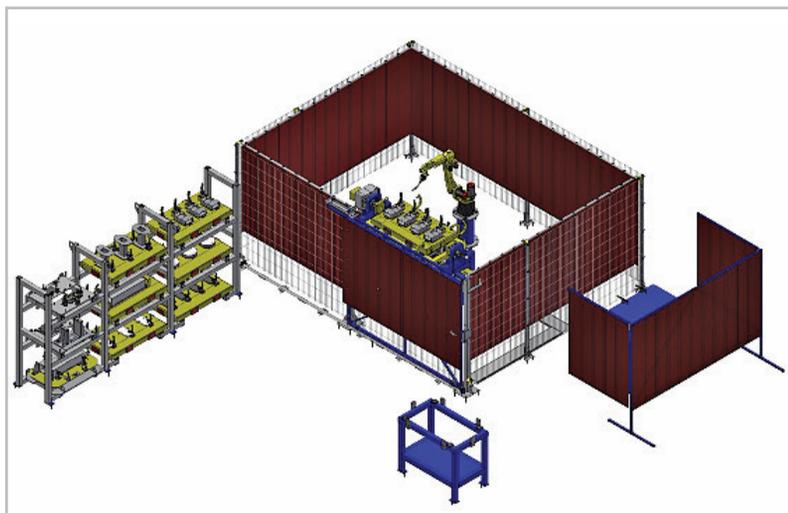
Общий вид роботизированной ячейки для сборки и сварки узлов тележки трамвая.
